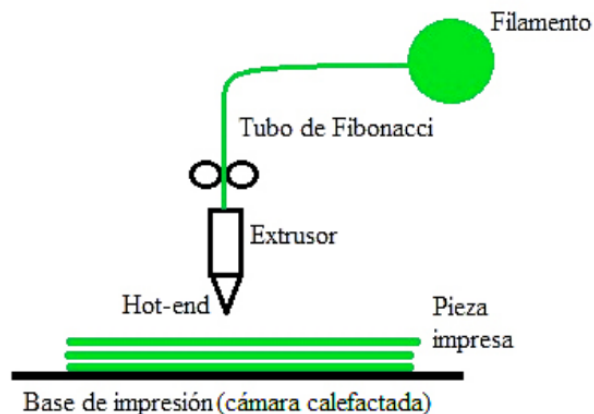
Esquema de una impresora 3D de modelado por deposición fundida (8)
